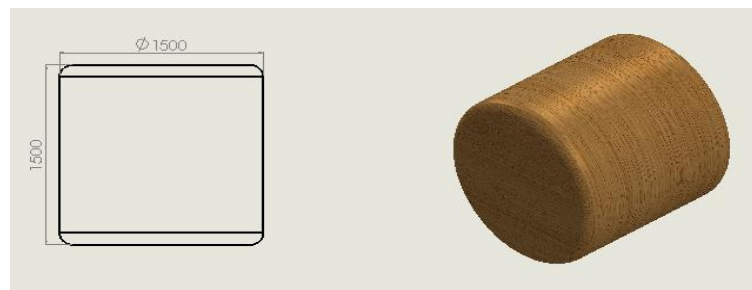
Vista en planta del rollo de alfalfa y sólido utilizado para el diseño del equipo.
